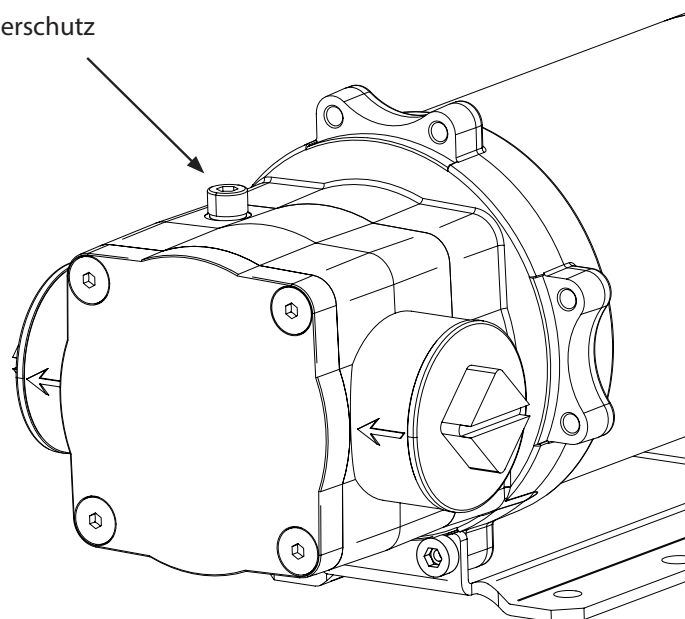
Bohrung für Heberschutz mit Schraube verschlossen (Lieferzustand)
